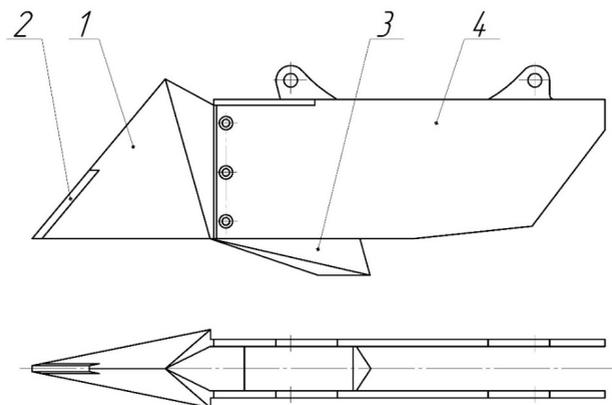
Патент UA 159673: 1 – робоча поверхня; 2 – плоский носок; 3 – п'ята; 4 – шок
